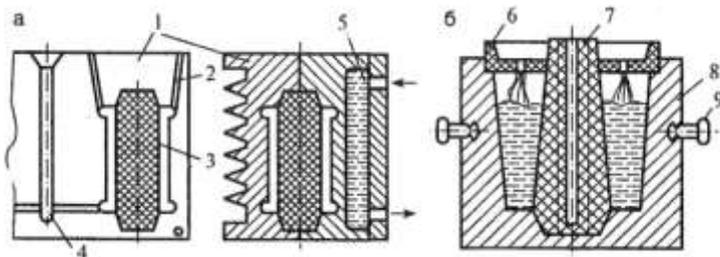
Конструкция кокилей: а – разъемный кокиль; б – вытряхной кокиль; 1 – полуформы; 2 – вентиляционные канавки; 3 – стержни; 4 – литниковые каналы; 5 – полости для охлаждения; б – заливочная чаша; 7 – стержень; 8 – вытряхной кокиль; 9 – опорные цапфы.
